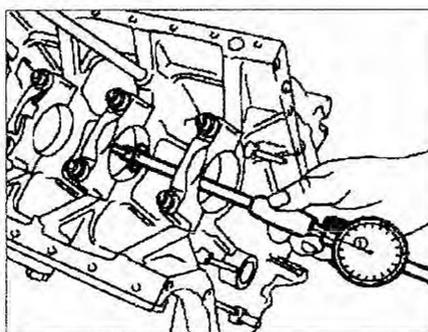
б. Измерение диаметра отверстия под коленчатый вал.
